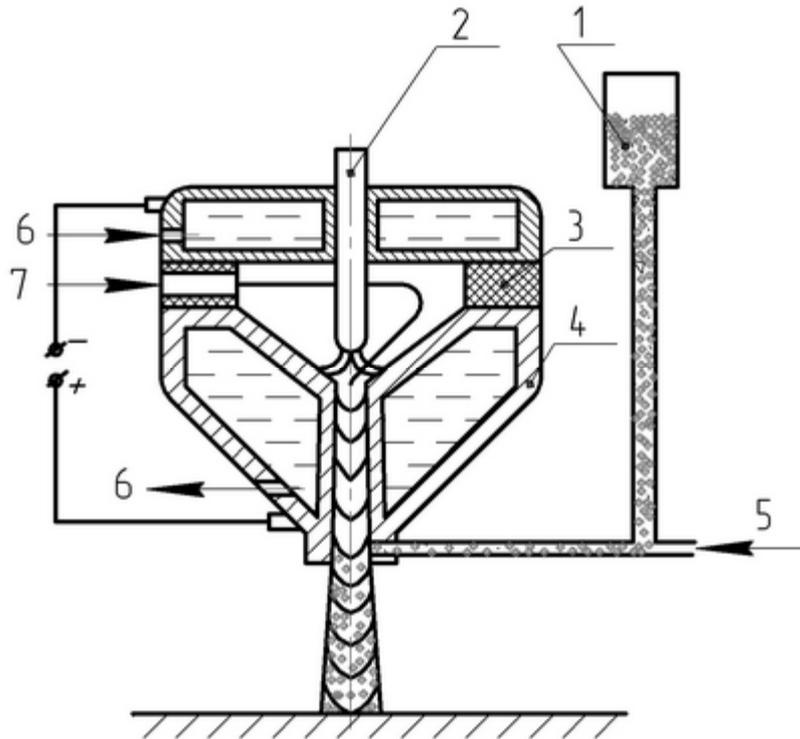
Схема плазменного напыления: 1 – порошковый дозатор; 2 – катод; 3 – изоляционная прокладка; 4 – анод (сопло); 5 – транспортирующий газ; 6 – охлаждающая вода; 7 – плазмообразующий газ
